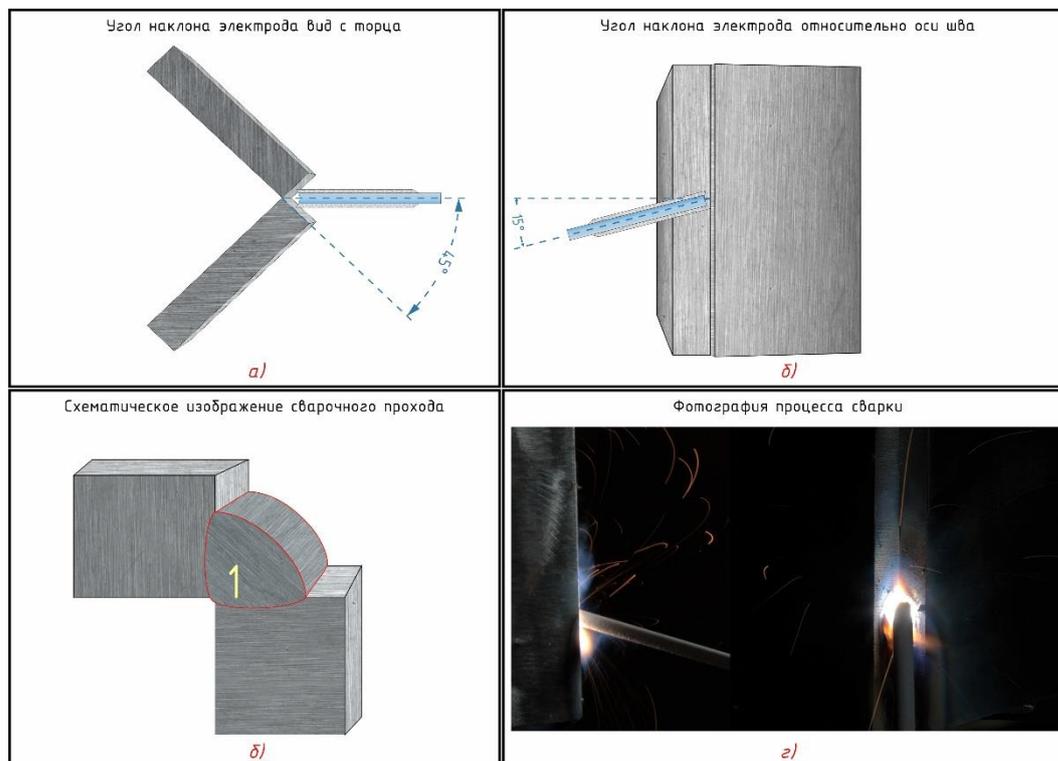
Положение электродов при сварке корневого прохода
